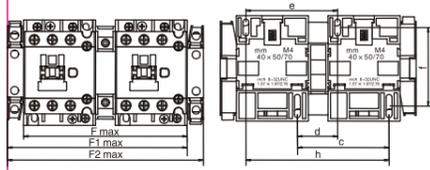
Габаритные и установочные размеры контакторов с реверсивной сборкой на токи 9А-38А, мм.
